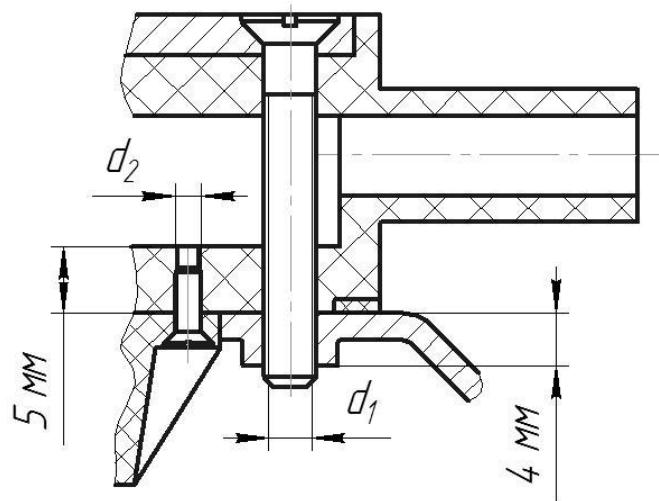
Схема до розрахунку різьбового з'єднання.
